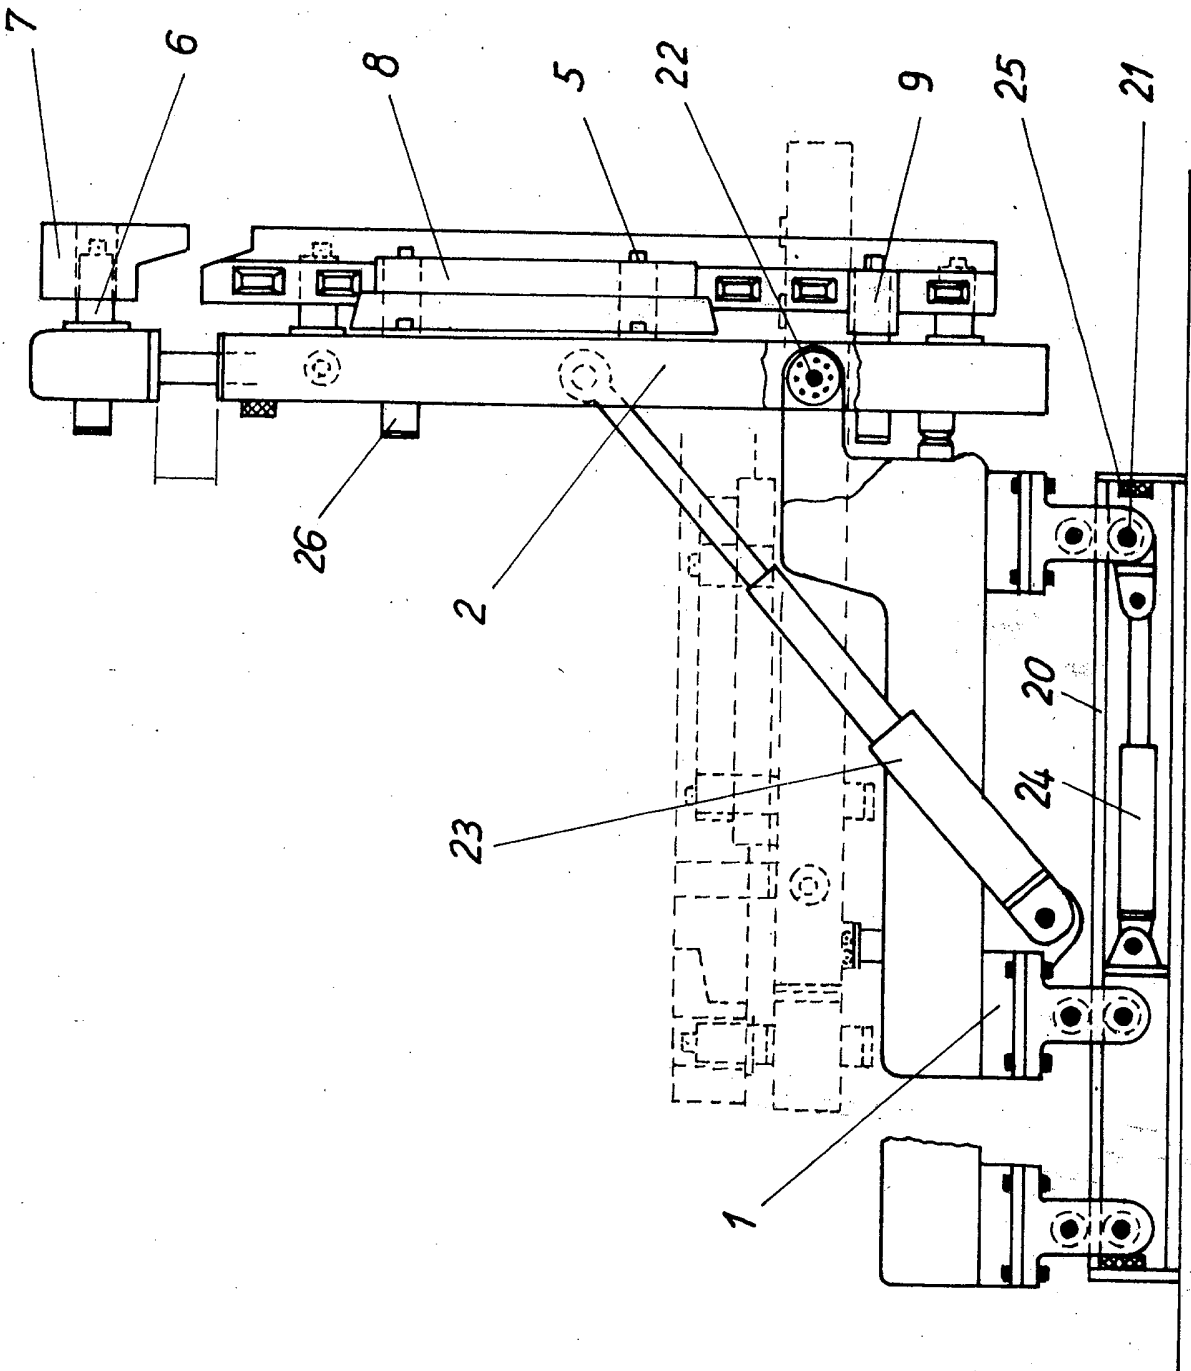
ukazuje provedené upevnění bednění 8 na tvářecí stěně před stažením desky 2 manipulátoru a obr. 8 ukazuje desku manipulátoru, uvolněnou od bednění 8 případně ze záběru s upínacím ústrojím 5.
